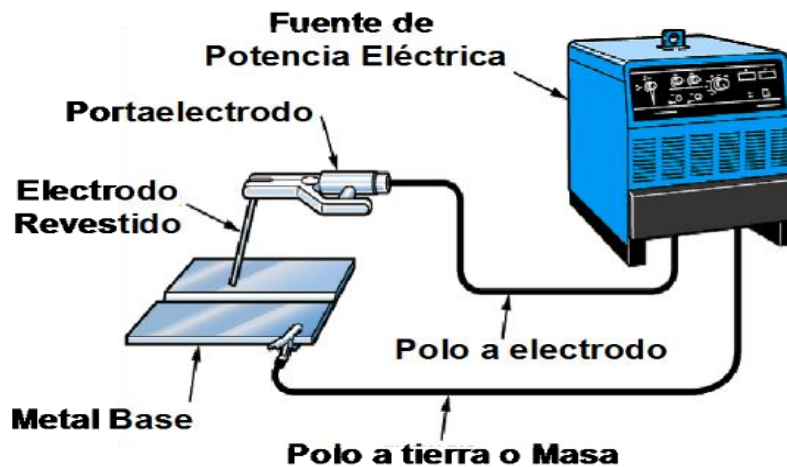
Soldadura por arco de metal protegido (SMAW).
